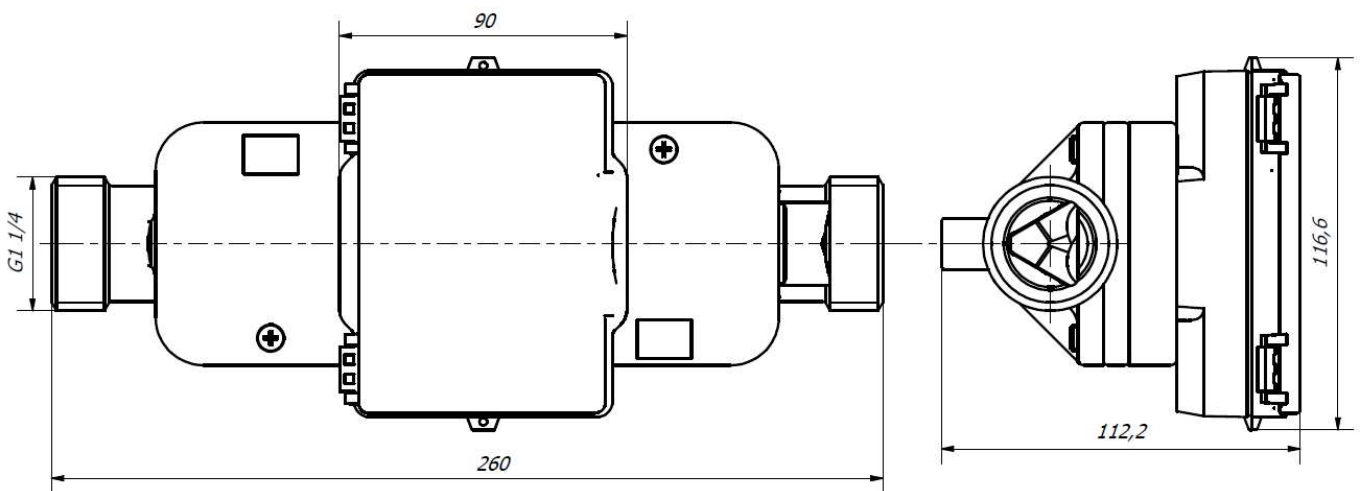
Gjengede endetilkoblinger G1 1/4", monteringslengde L=260 mm.
